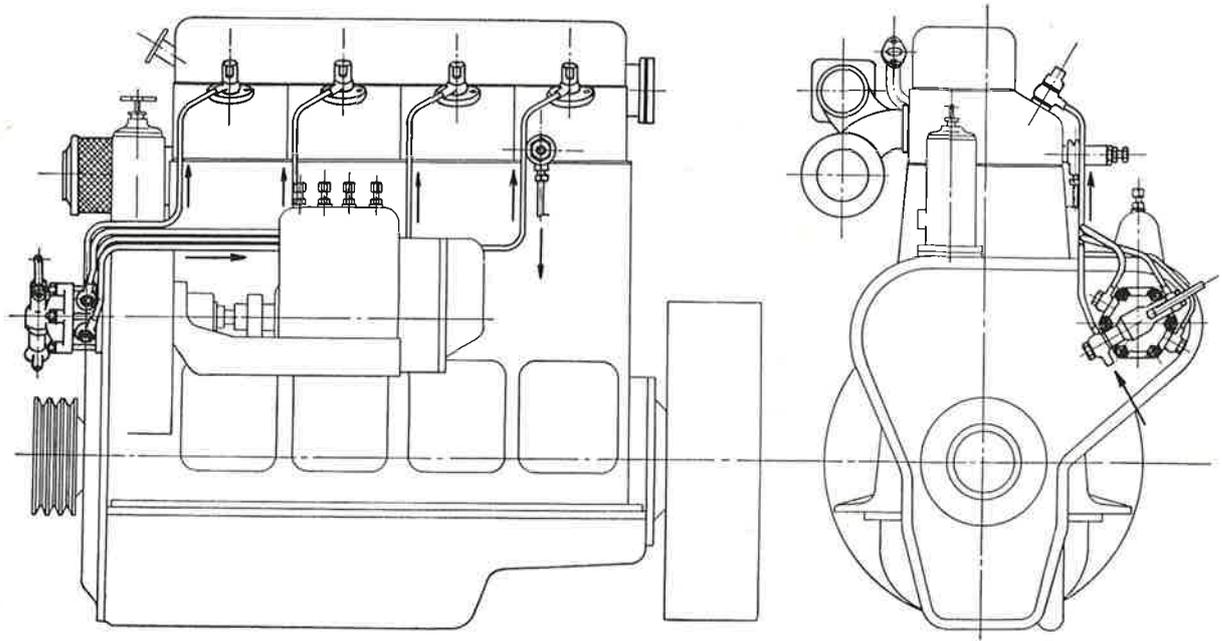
Schema der Druckluft-Anlassvorrichtung
